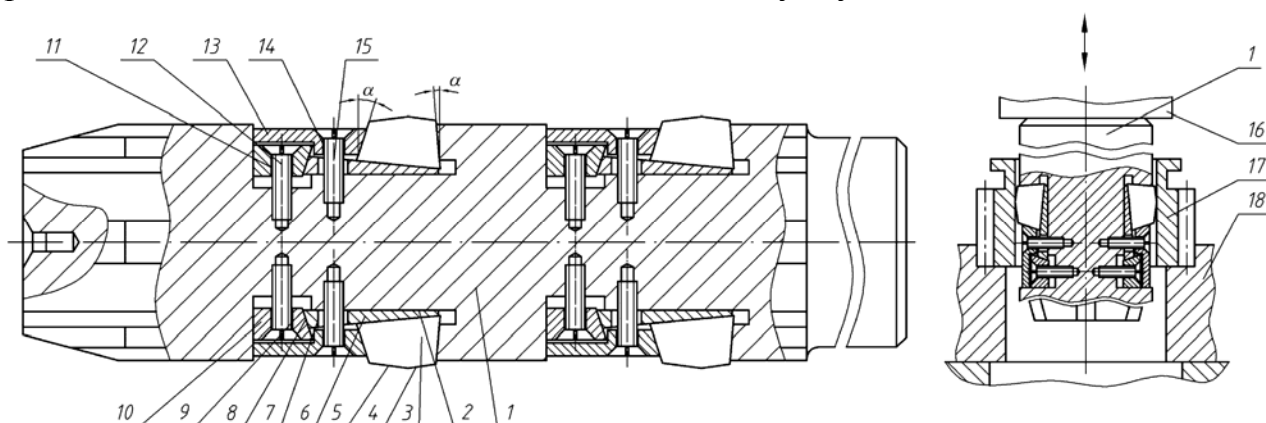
Конструкція дорна для обробки шліцевих отворів
